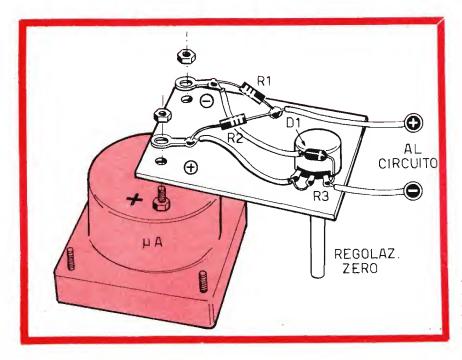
Cablaggio del ponte a diodo riportato in figura 3. Il diodo D1 deve essere inserito nel circuito secondo la polarità indicata nel disegno (fascetta colorata).
